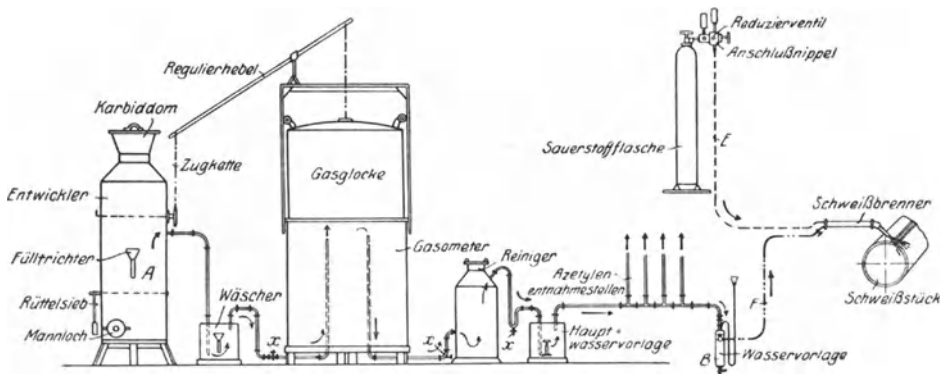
Schema einer Azetylen-Schweißanlage,
